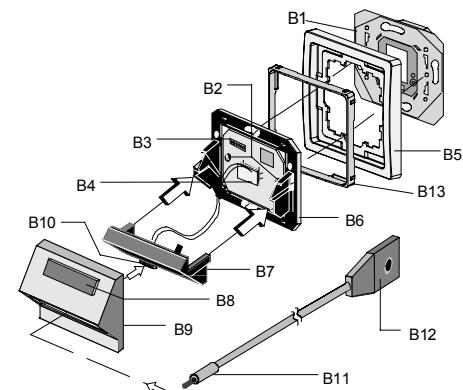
Einbau des Unterputzgerätes mit Wasserfühler
